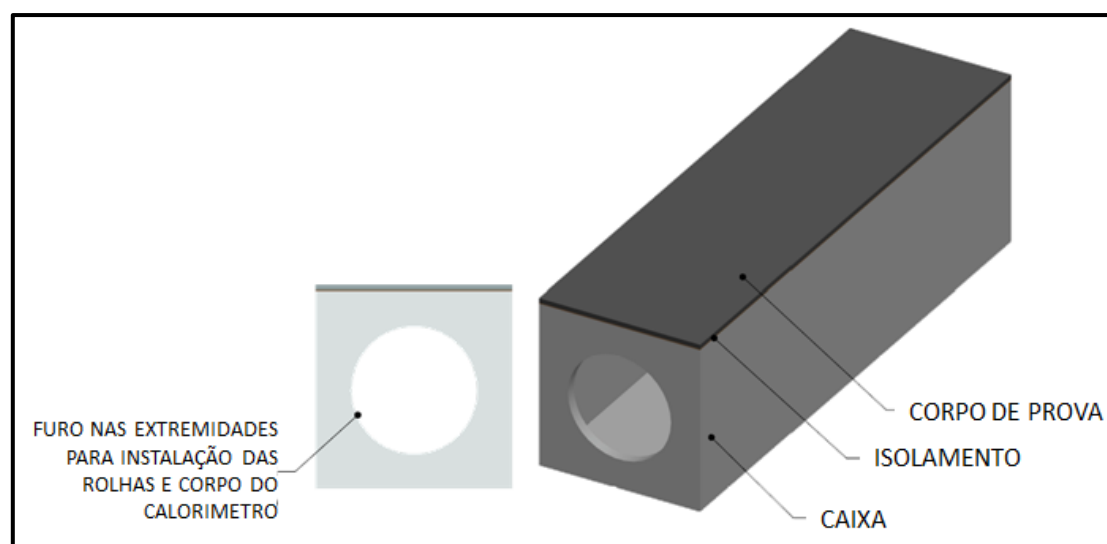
Proposta de caixa para ser utilizada na medição do aporte térmico na soldagem de chapas metálicas.
